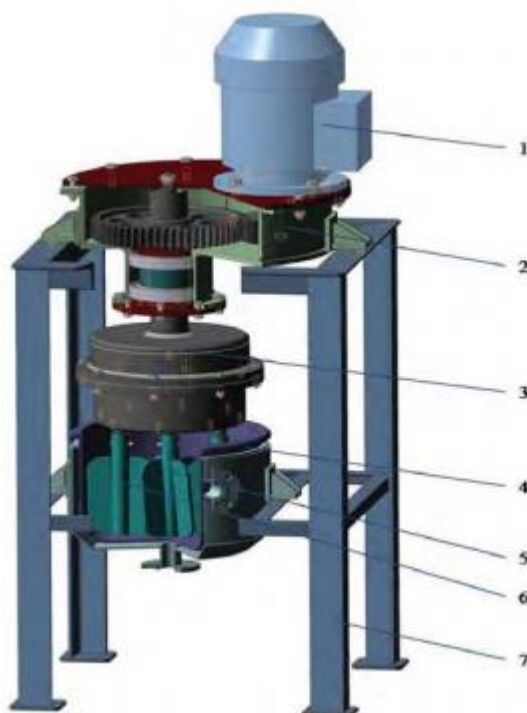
Лопастной смеситель планетарного типа для смешивания дисперсных материалов с вязкими средами: 1- двигатель; 2-привод; 3- редуктор; 4-камера смешения; 5,6-мешалки;7-стойка.
